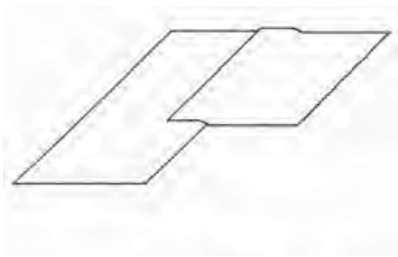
Tipo de ligação de superfície (junta soldada) [2].
